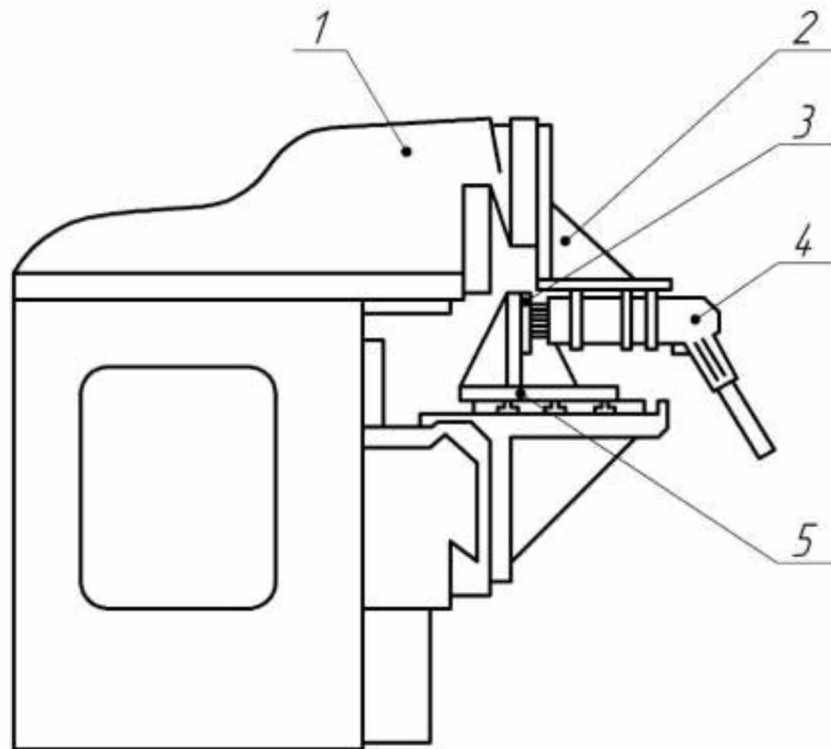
Схема обладнання вертикально-фрезерного верстата для формування РМР на плоских поверхнях за допомогою КСЗ
